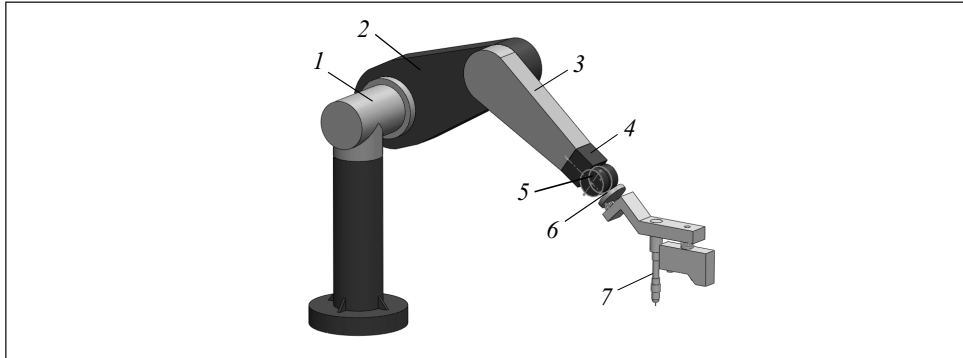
Кинематическая схема сварочного робота: 1–6 — звенья робота; 7 — сварочная горелка
